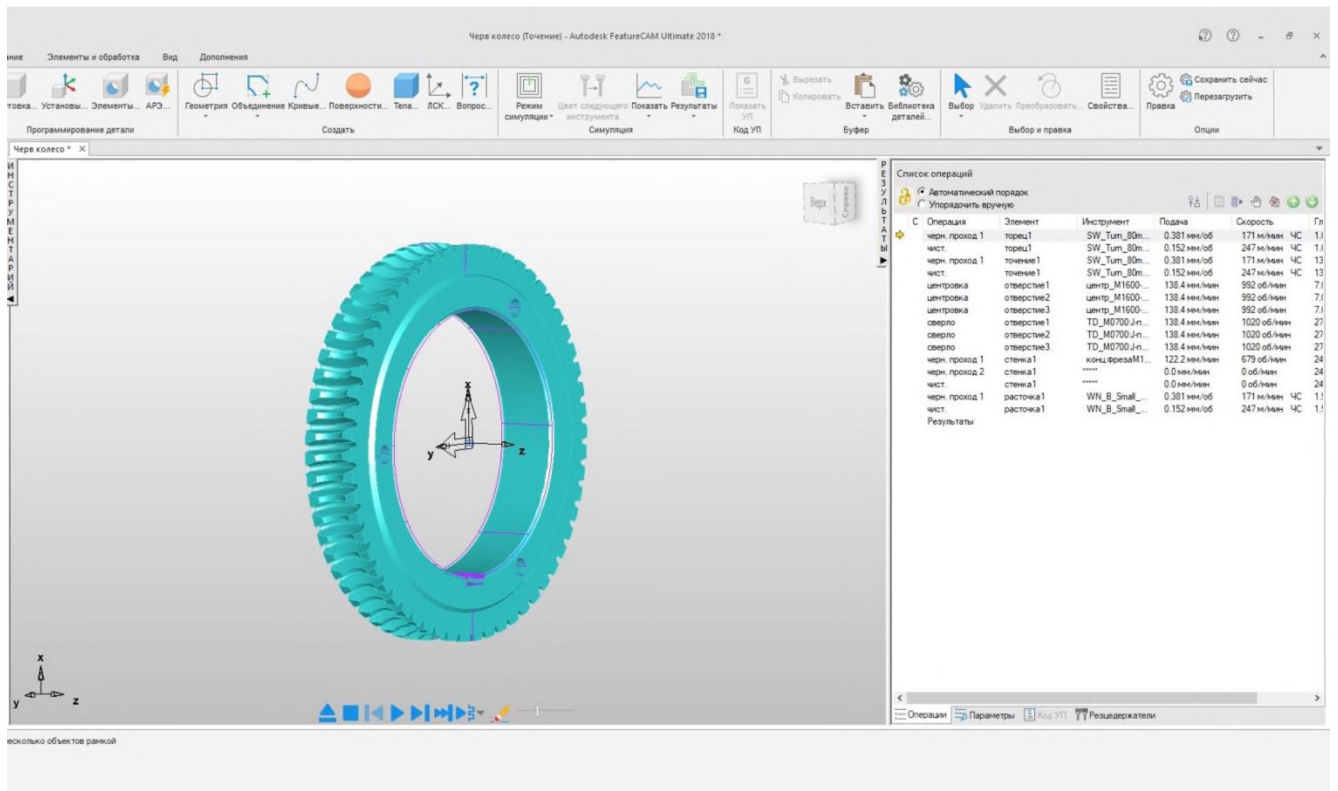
Этапы обробки деталі «Колесо черв’ячне»
